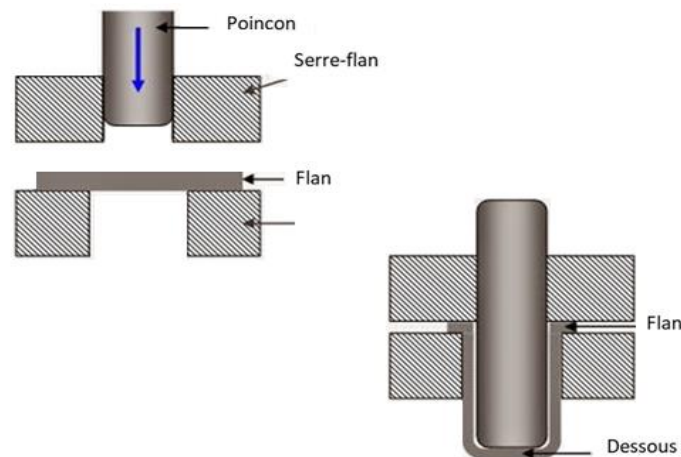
Principe d'emboutissage (pièces forgées) .
